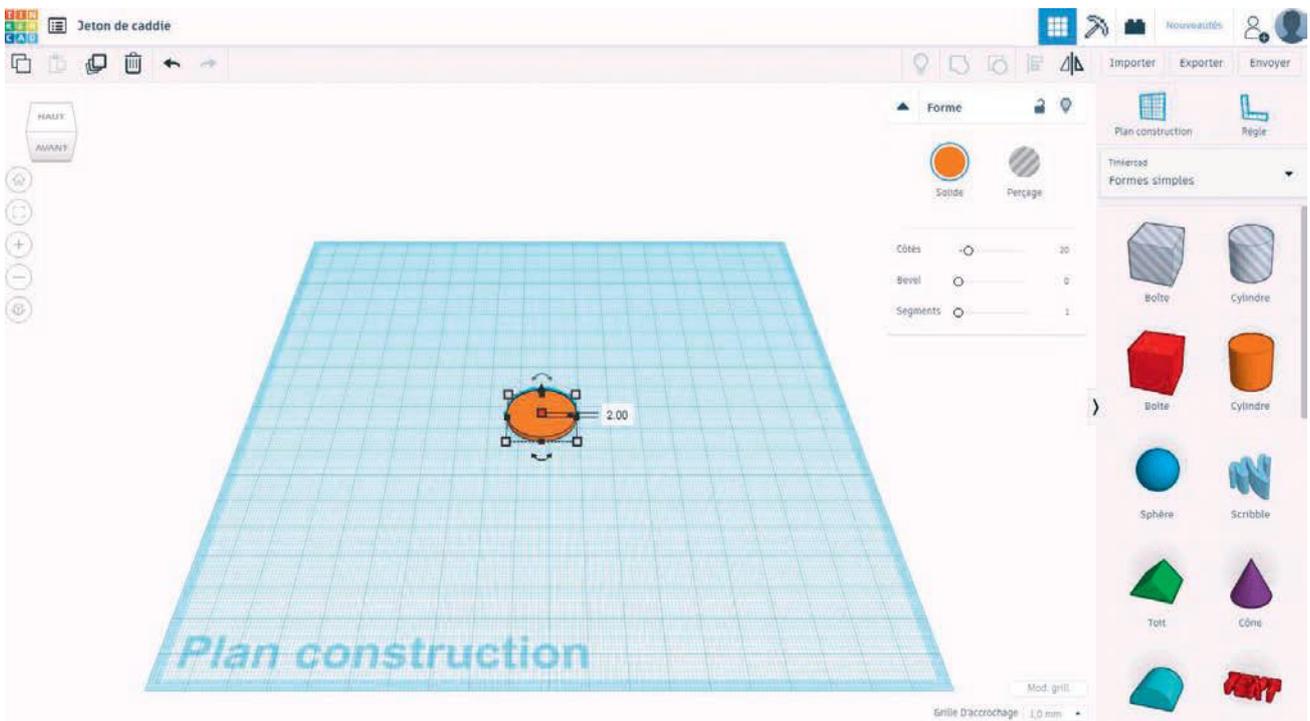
Projet « Jeton de caddie » - Préparation finale de la pièce (définition de la hauteur)
